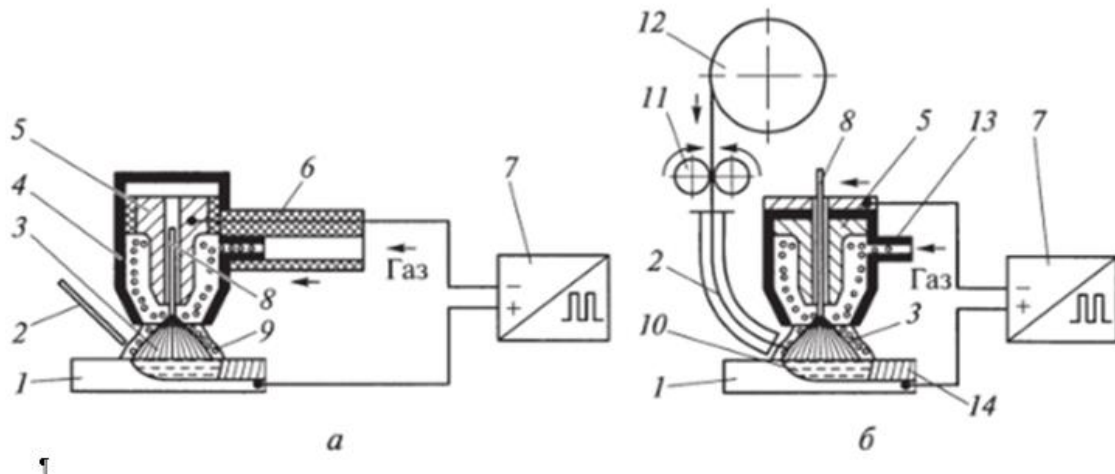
Схеми ручної (а) і напівавтоматичного (б) пальників для зварювання неплавким електродом:
